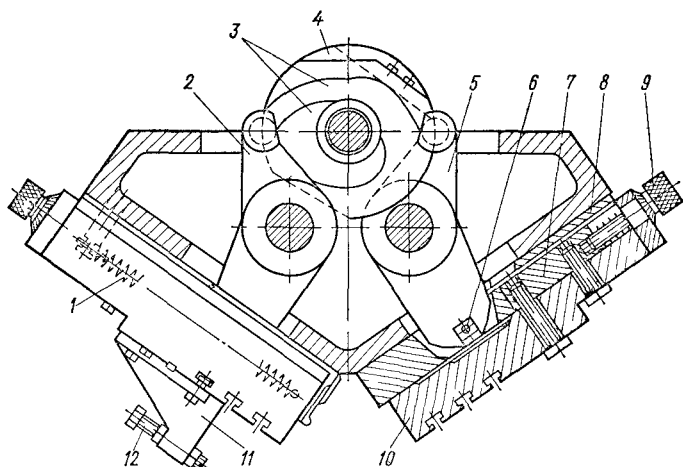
Механизмы перемещения поперечного верхнего суппорта
